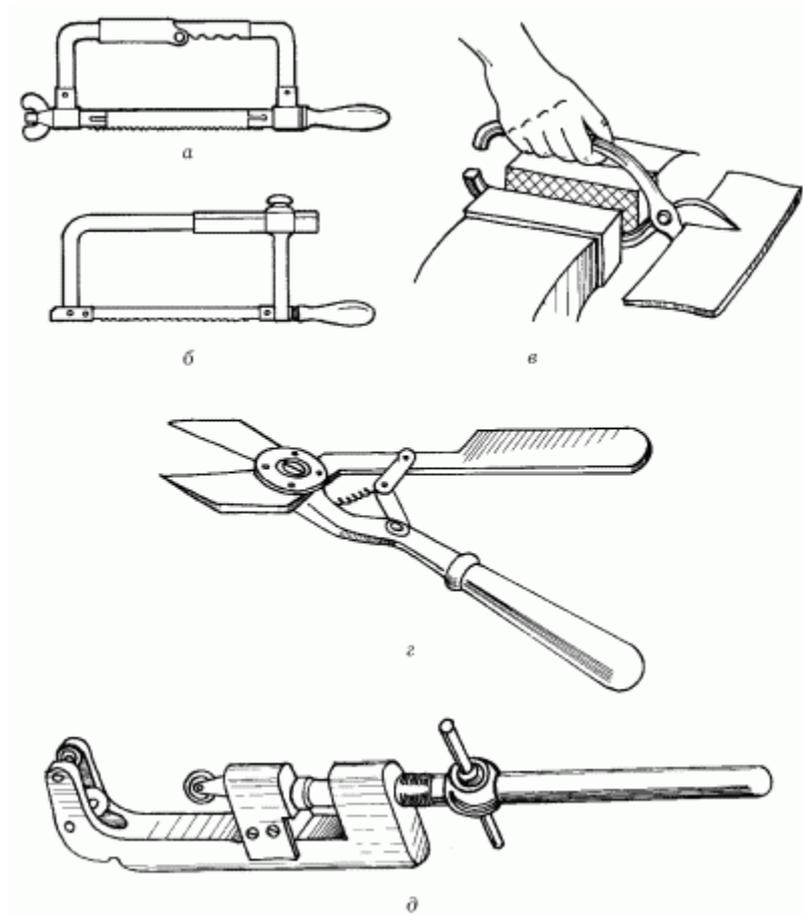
Инструменты для резки металла: а – ножовка; б – лобзик; в – ручные ножницы; г – силовые ножницы; д – труборез.
